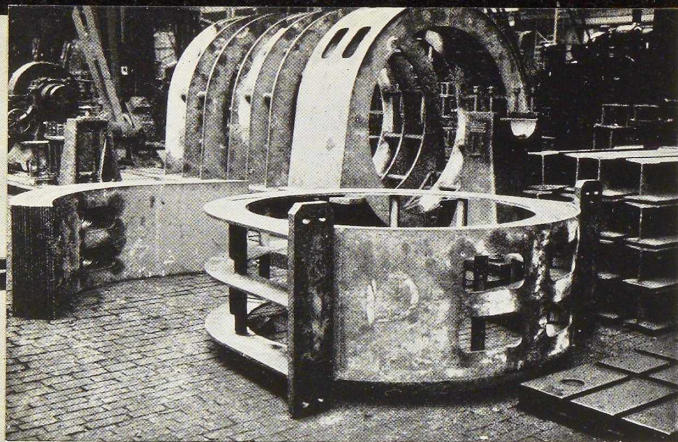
Flasques, carcasses, pattes de fixation et poutrelles découpés par la coupeuse automatique et assemblés par soudure (S. E. M. à Gand).
